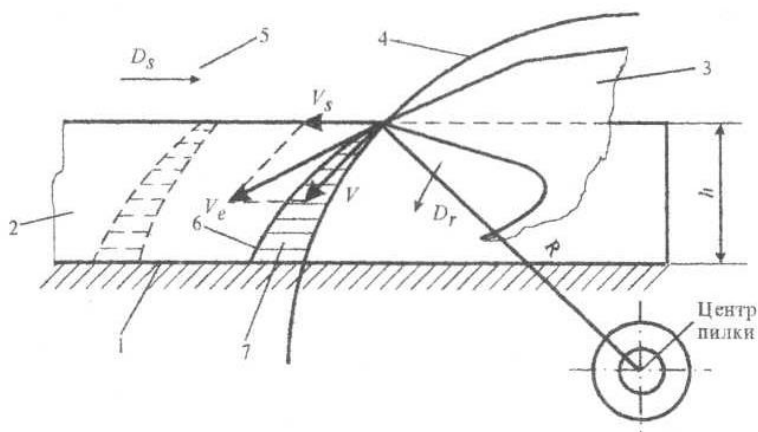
Схема різання зубом круглої пилки: 1 - базова поверхня; 2 - заготовка; 3 - зуб пилки; 4 - траєкторія переміщення вершини зуба; 5 - траєкторія переміщення заготовки; 6 - абсолютна траєкторія переміщення вершини зуба в матеріалі; 7 - стружка
